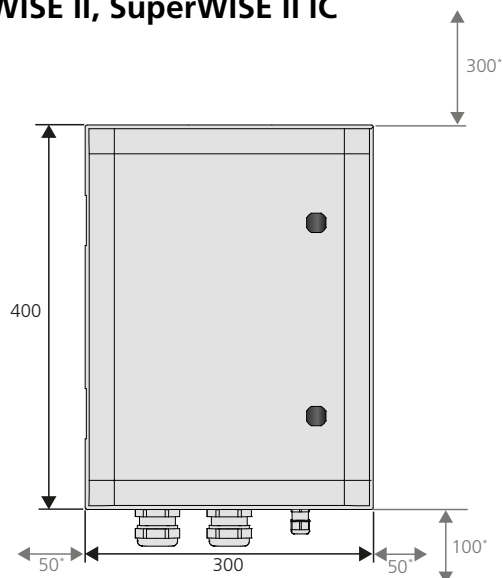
SuperWISE II, SuperWISE II IC, esquema de dimensiones.
